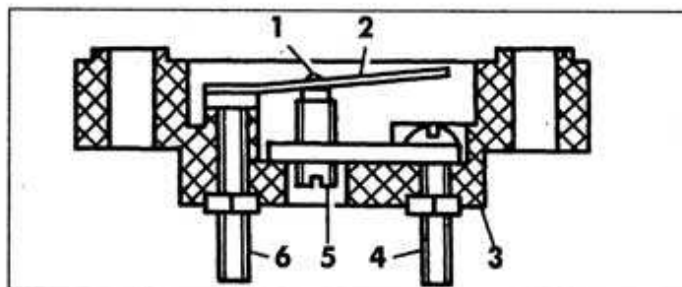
Биметаллический предохранитель стеклоочистителя: 1 – контакт; 2 – биметаллическая пластина; 3 – корпус; 4 и 6 – выводы; 5 – регулировочный контакт
